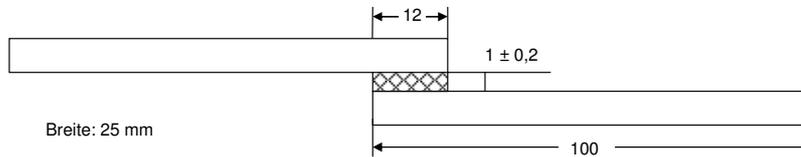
Probekörper nach DIN 32622, Abschnitt 4.4.2.2 c)
